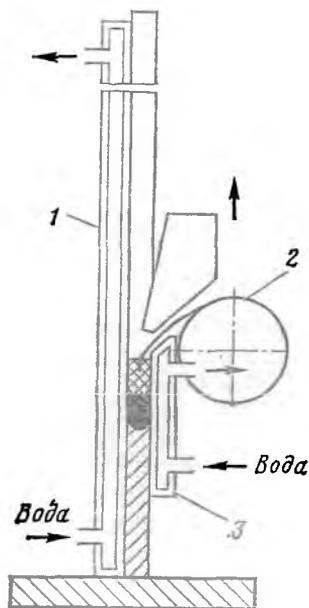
Схема вертикальной автоматической сварки: 1 — неподвижная накладка; 2 — сварочный автомат А-820М; 3 — подвижная накладка (ползун)
